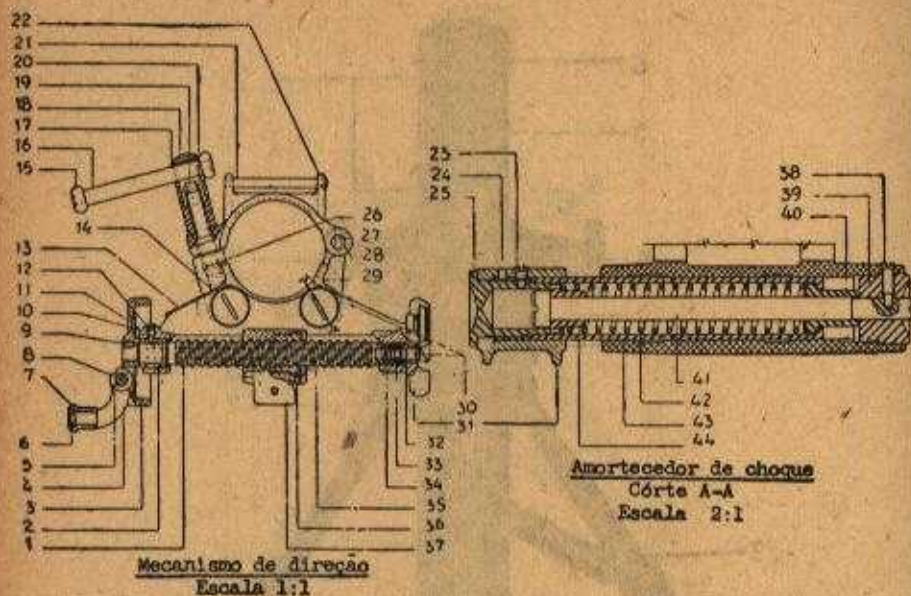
Morteiro de 60 mm — Mecanismo de direção e amortecedor — Vista seccionada
